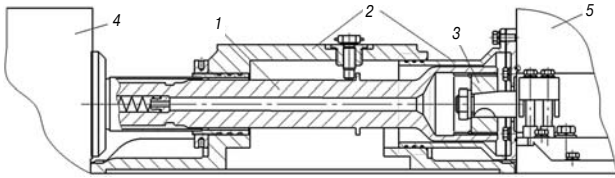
Общий вид базовой конструкции привода ТНВД дизеля 8СН21/21:
